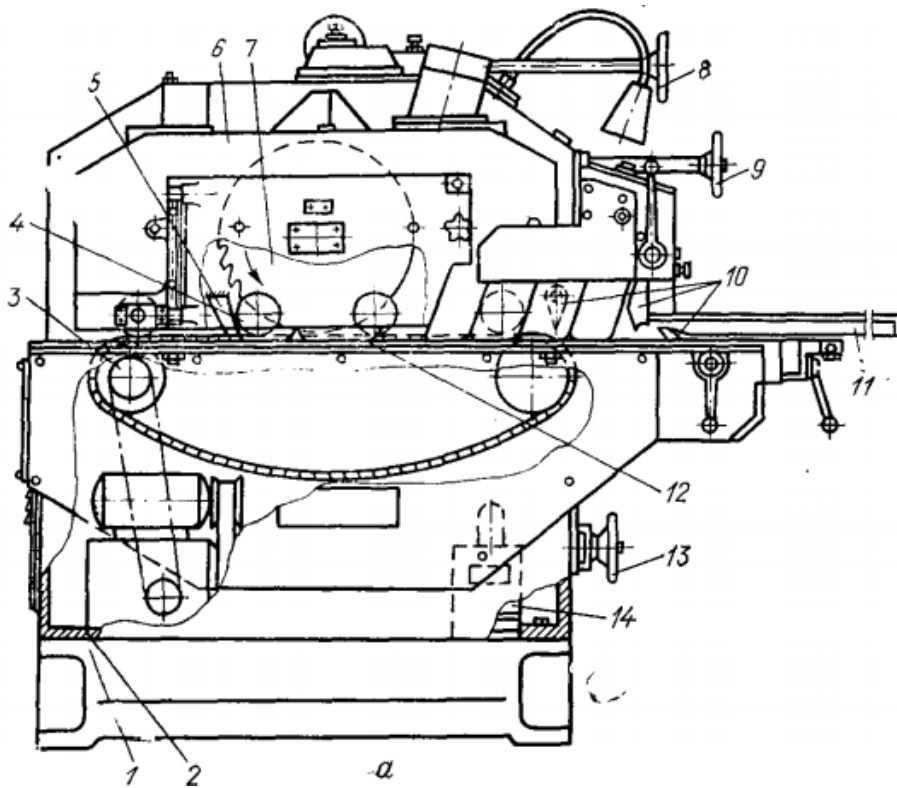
Конструктивний склад деревообробного верстату ЦДК5
